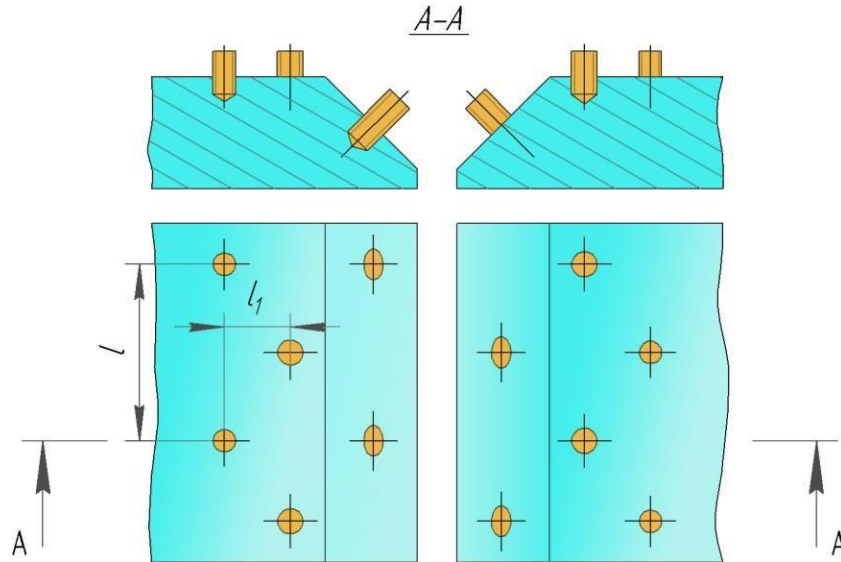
Підготовка чавунних деталей під зварювання за допомогою шпильок
